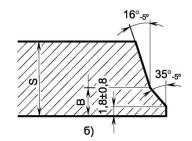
Форма разделки кромок труб для комбинированной сварки с применением Комплекса автоматической сварки
